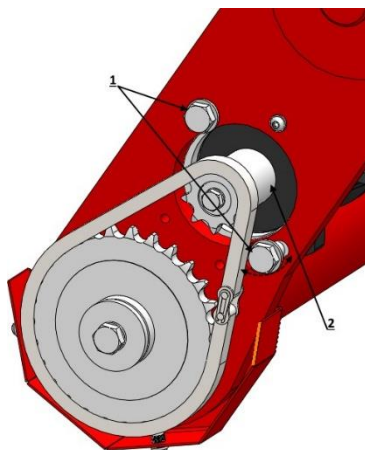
Регулировка цепи привода нижних обматывающих рычагов
